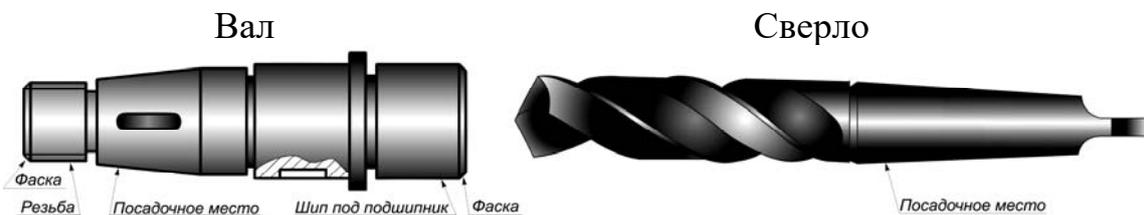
Примеры деталей с коническими поверхностями
